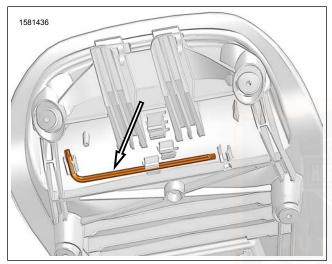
Herramienta de ajuste del faro delantero (si está equipado)
